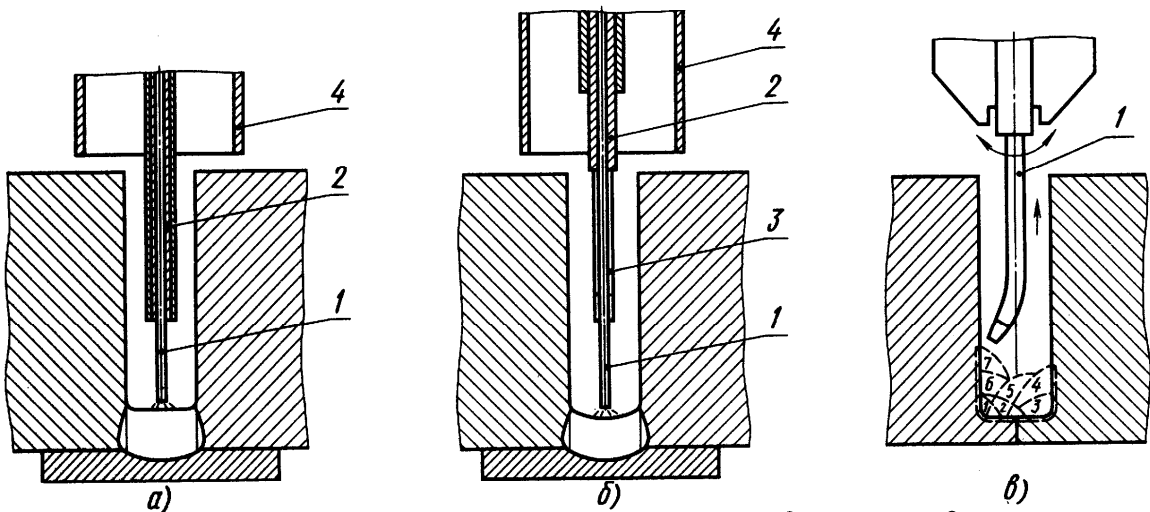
Схемы подачи электродной проволоки в сварочную ванну
